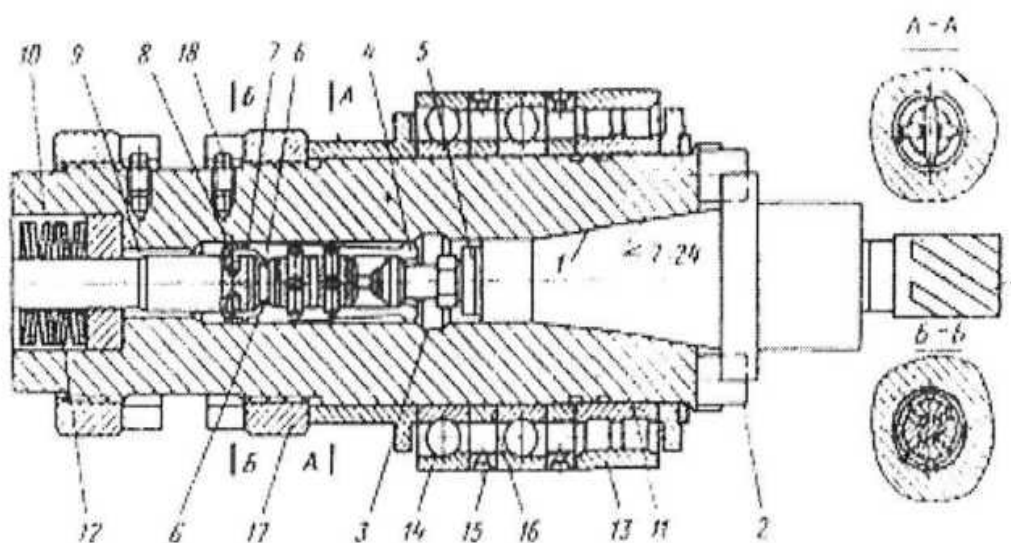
14. Елементи конструкції шпинделів фрезерних верстатів.
